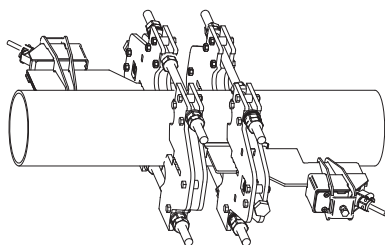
Установленный волновой инжектор WaveInjector (установка с резьбовыми шпильками)
